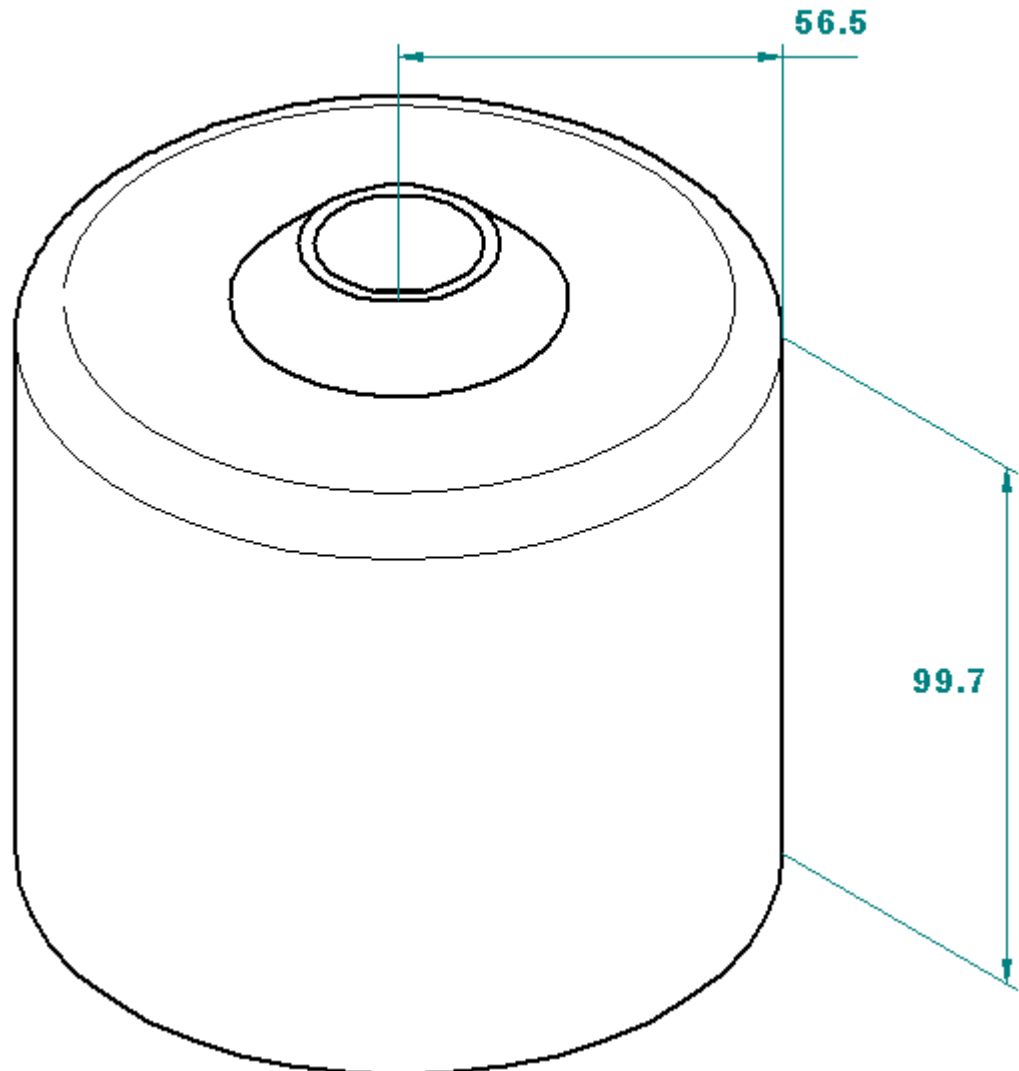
Dimensiones del Boiler de destilación TK6. [11]
